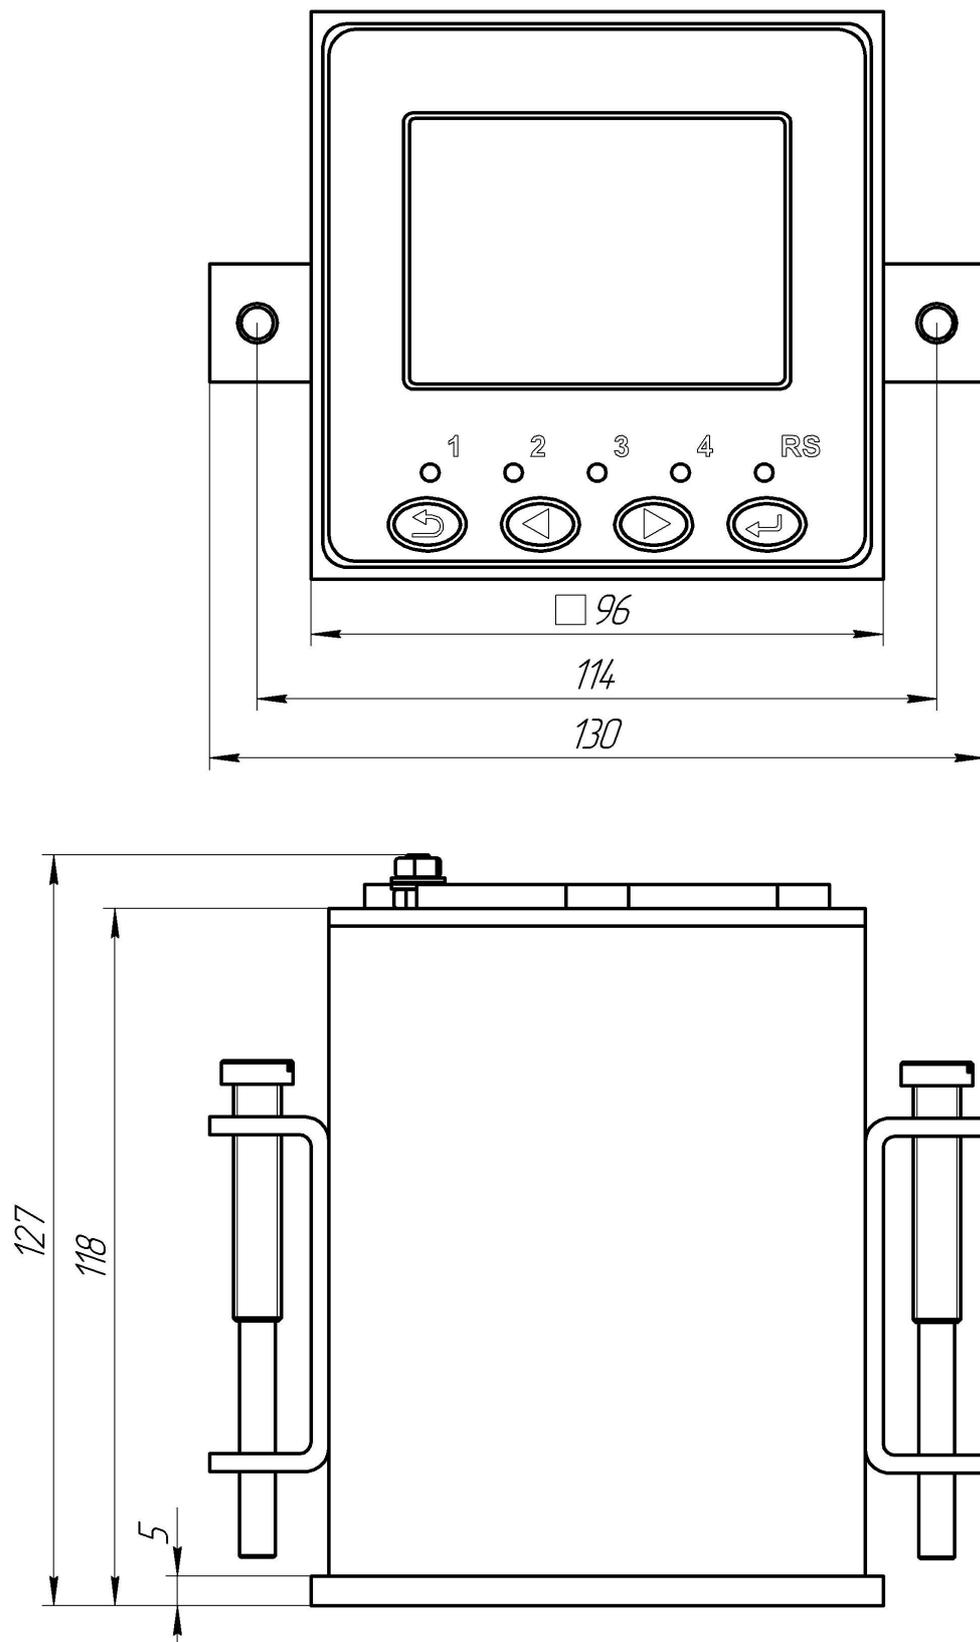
Габаритные размеры корпуса ИП щитового исполнения
